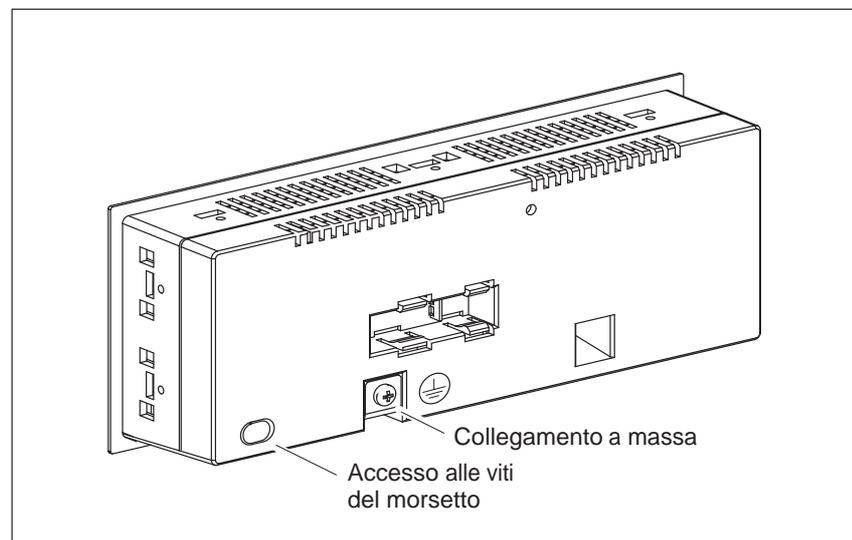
Accesso alle viti del morsetto e collegamento a massa
